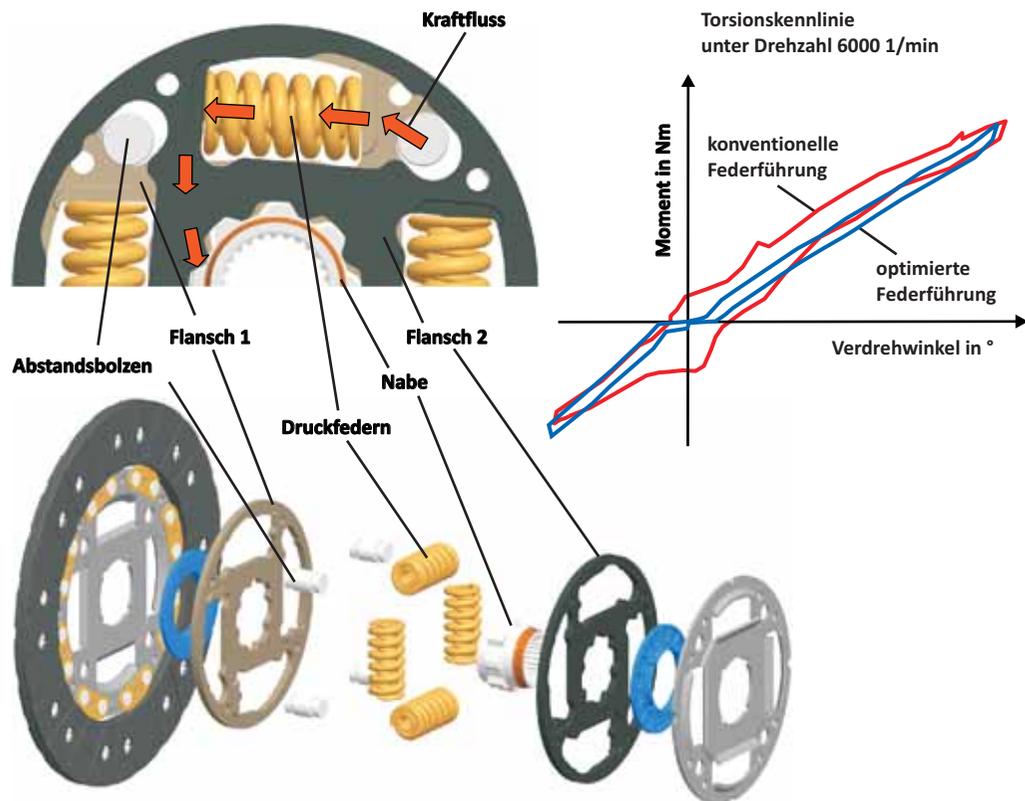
Dämpfer für Hybridanwendung mit optimierter Federführung
